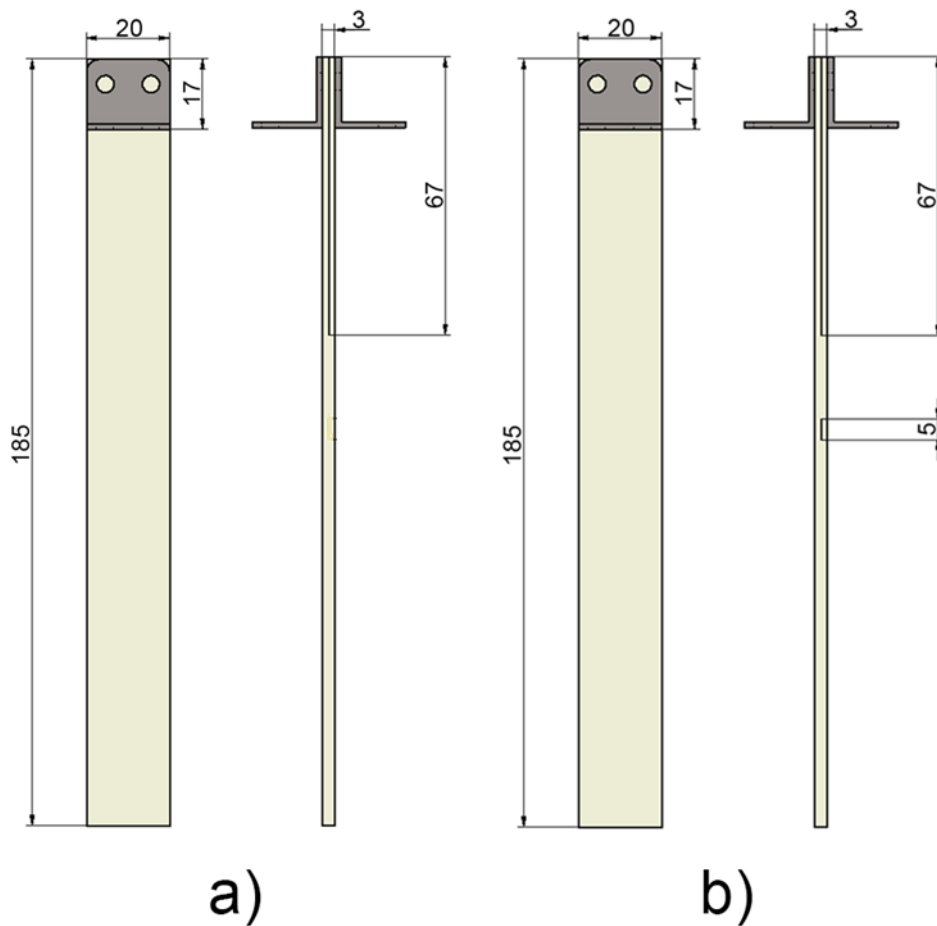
a) Probeta con una grieta. b) Probeta con dos grietas.
